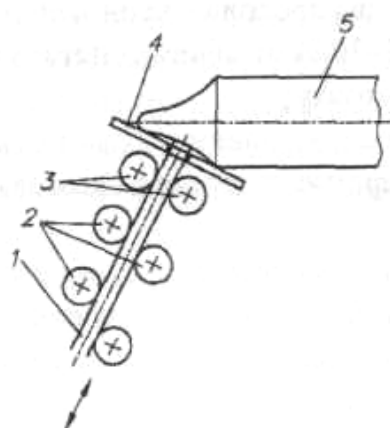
Схема обработки отверстий диаметром менее 0,6 мм: 1 – проволочный электрод-инструмент, 2 – система роликов для правки проволоки, 3 – подающие ролики, 4 – кондукторная втулка, 5 – обрабатываемая заготовка
